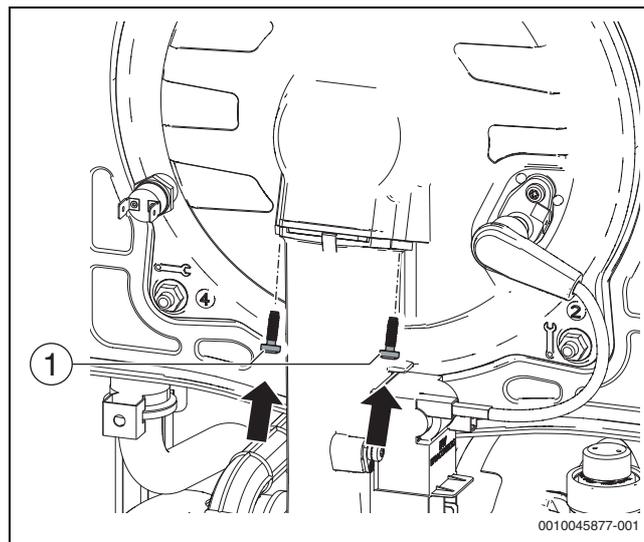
Montage du tube d'air pour gaz sur la porte foyer
